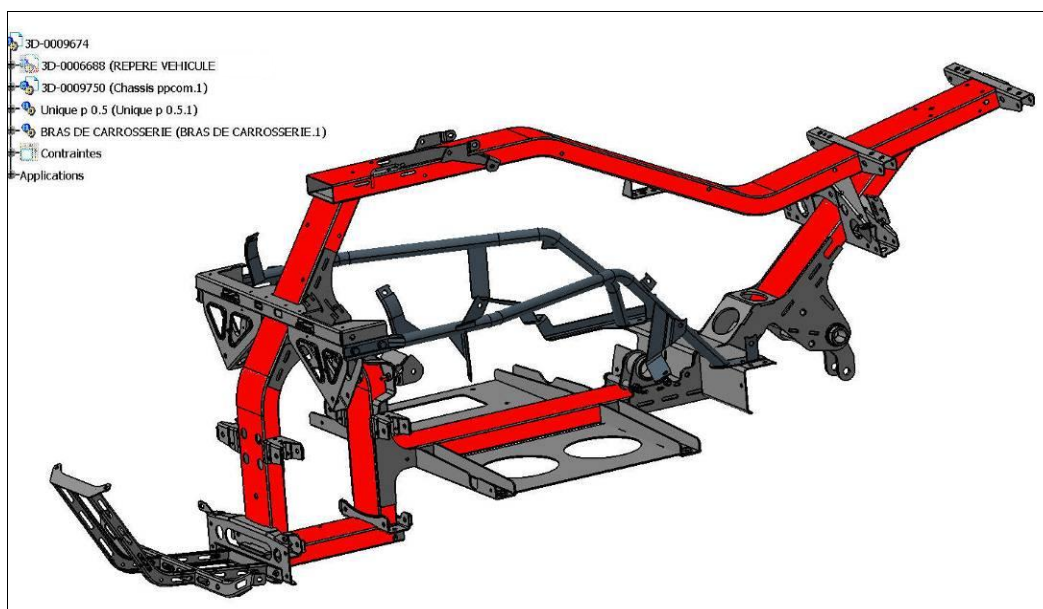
Ensemble châssis PROTOTYPE P\_0,5 optimisé aluminium [61]
